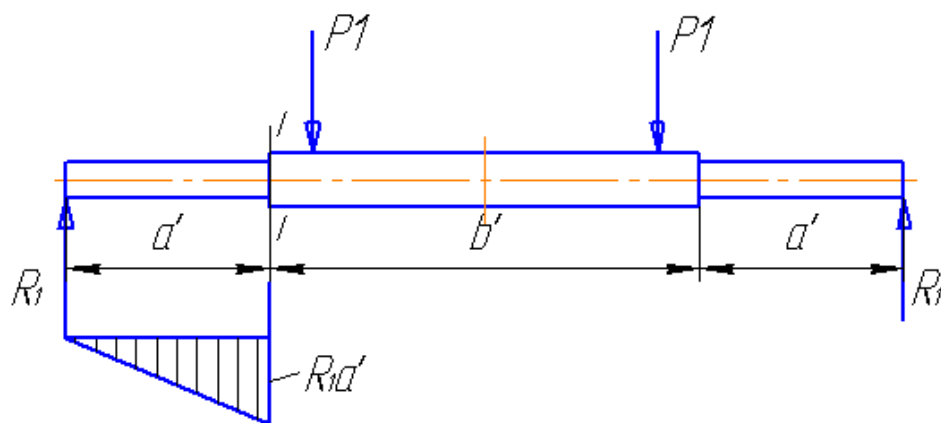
Розрахункова схема ходової частини обприскувача
